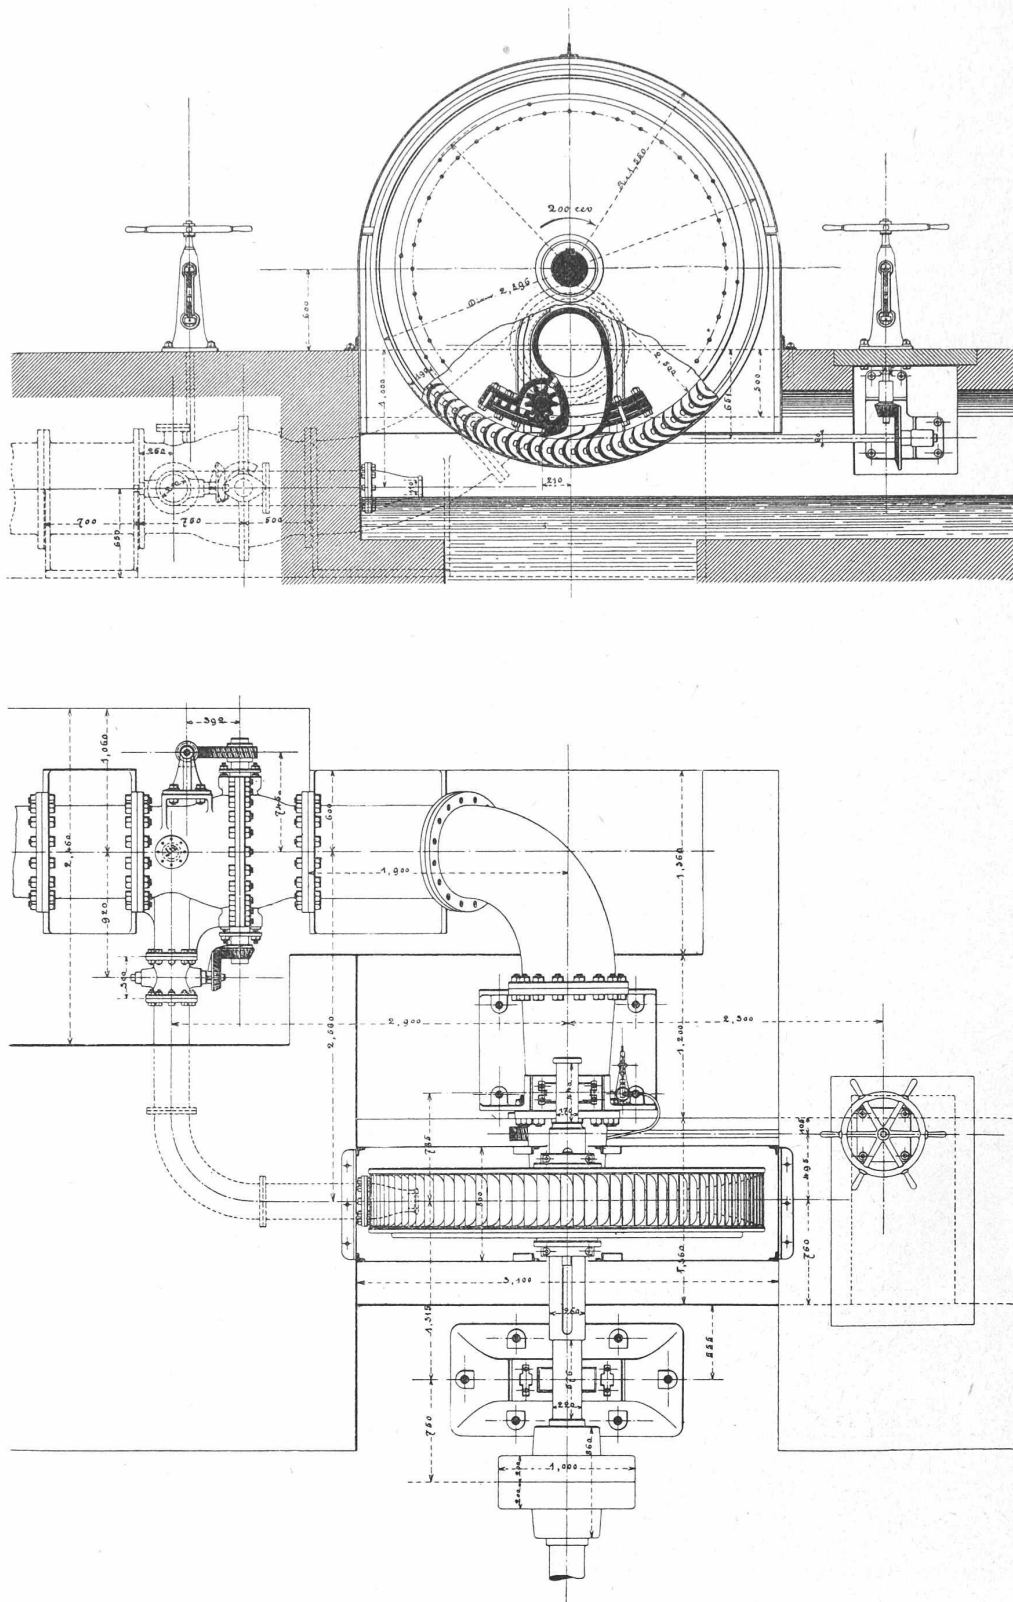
und 4. Ansicht und Grundriss.
